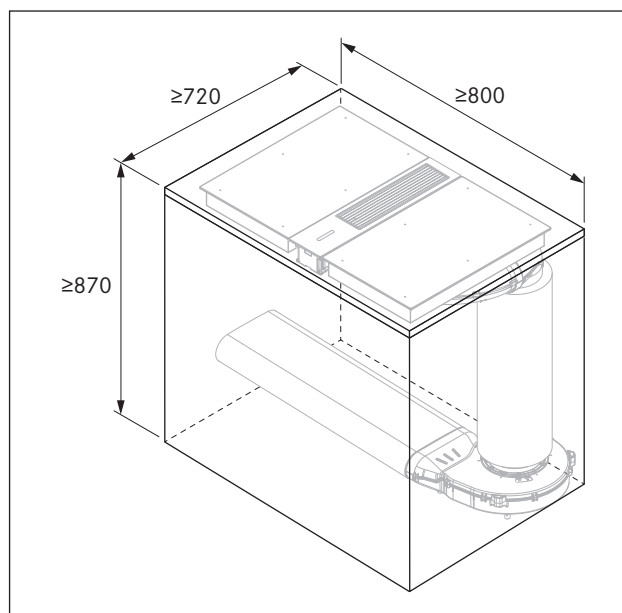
Dimensões mínimas de montagem com silenciador redondo USDR50
